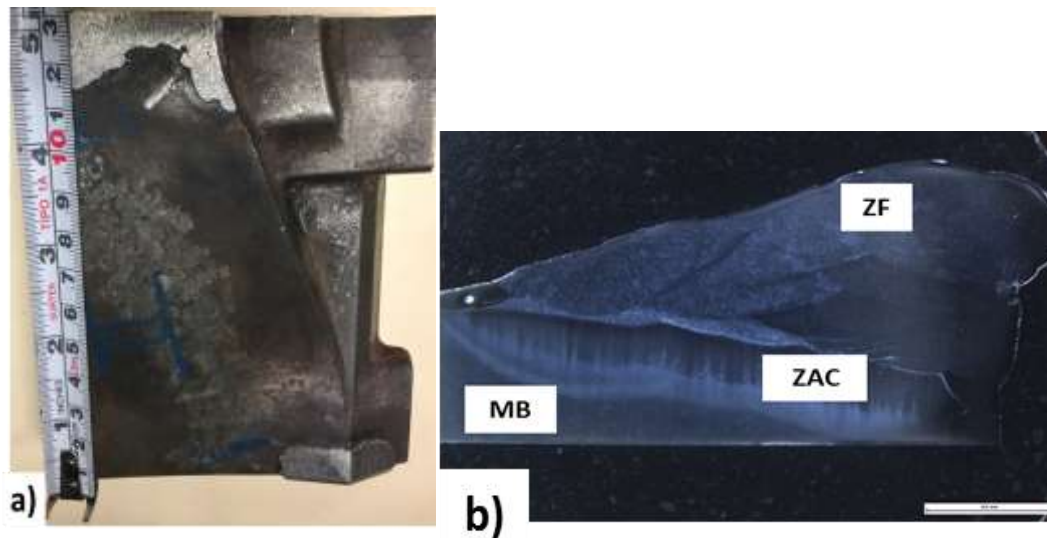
2 a) Inserto soldado, b) Corte transversal de inserto observado por microscopio óptico
